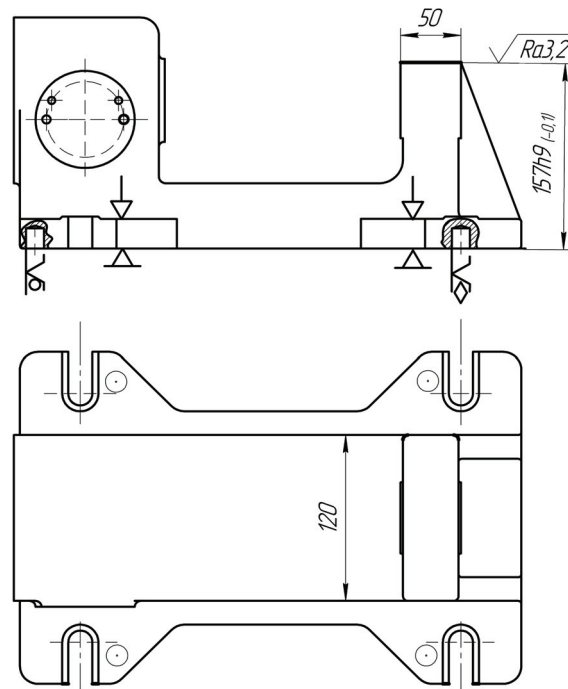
Ескіз обробки площини корпусної деталі в розмір 157h9 мм
